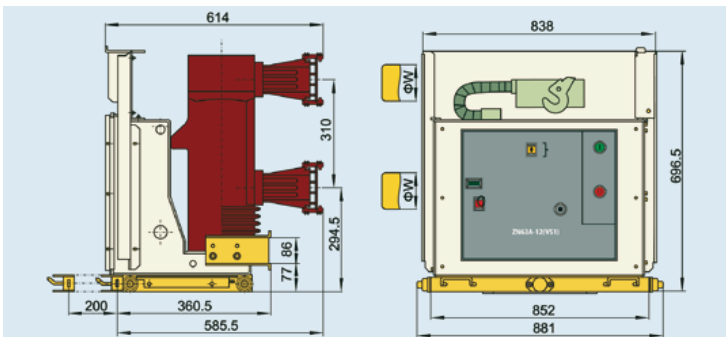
Внешний вид и монтажные размеры выключателей: ZN63A-12/T3150-40
